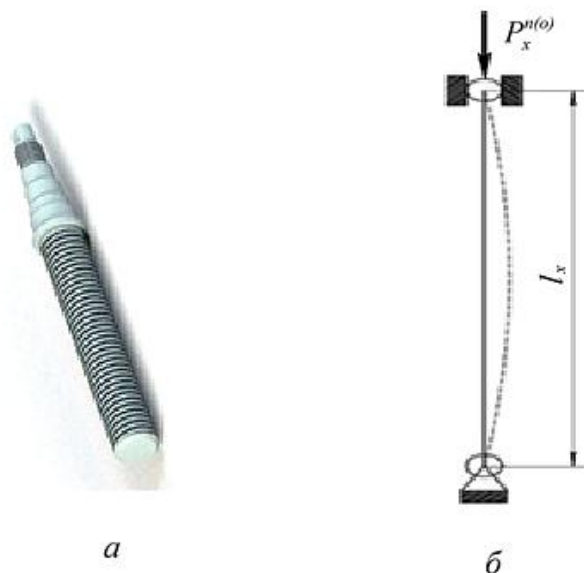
Ходовой винт (а) и его расчетная схема (б)
